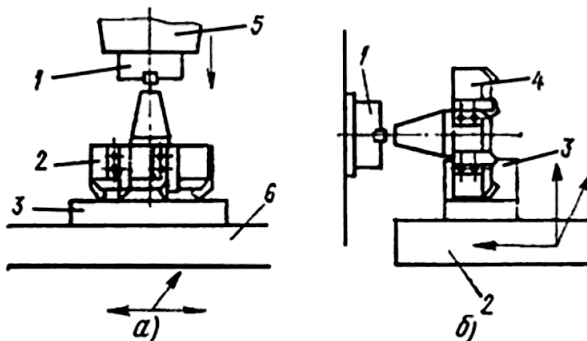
Способы установки на станке крупных и тяжелых фрез
